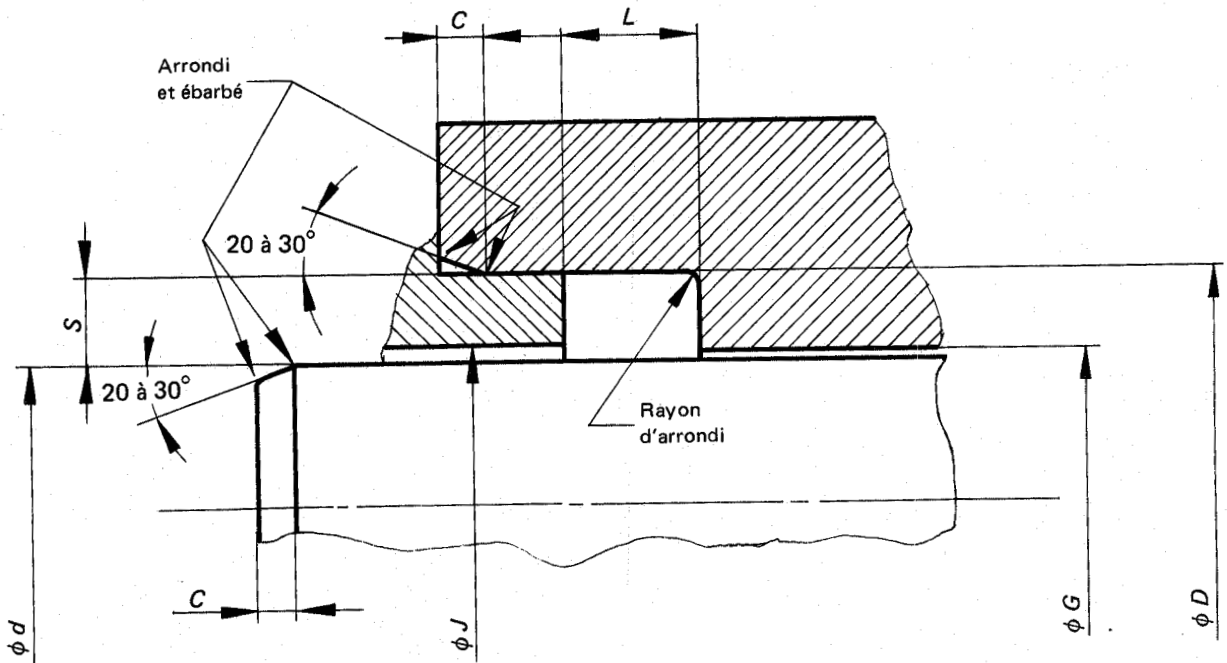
Exemple de logement de joint d'étanchéité pour tige de piston
